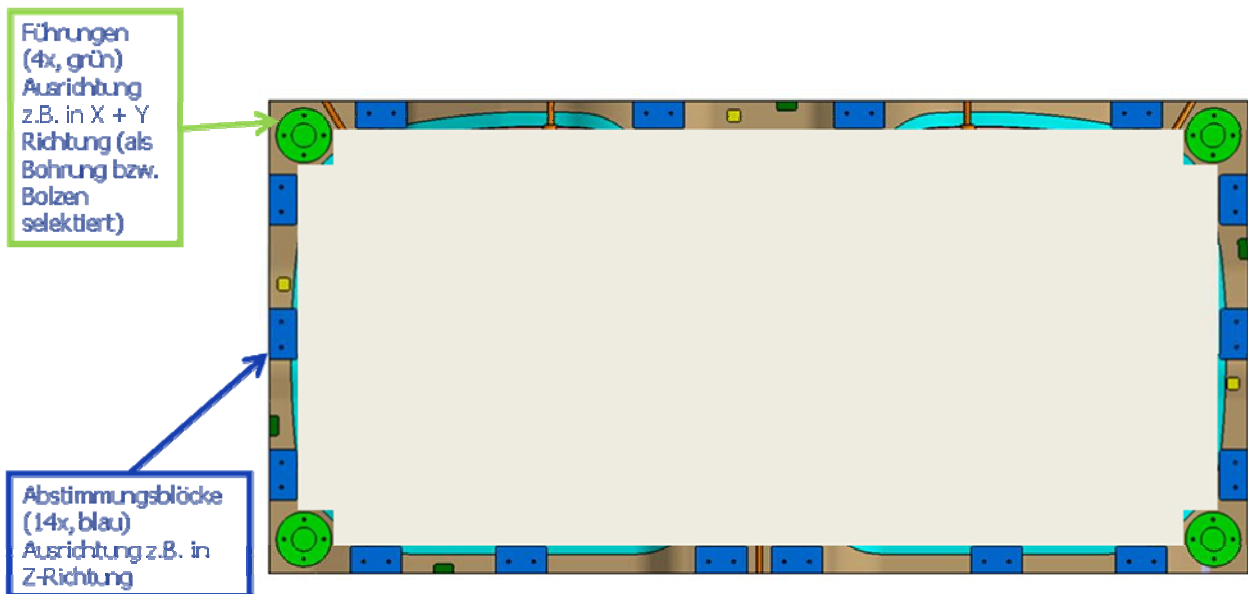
Ausrichtung für Werkzeuge, Formen und Vorrichtungen
